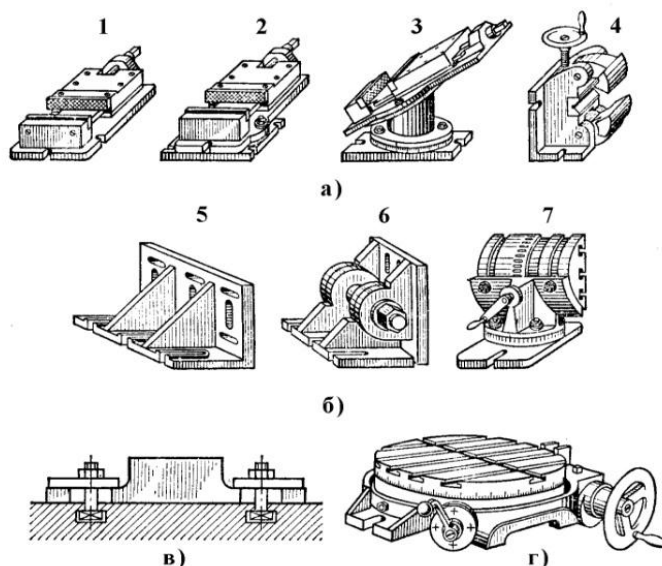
Приспособления для закрепления заготовок на фрезерных станках:
